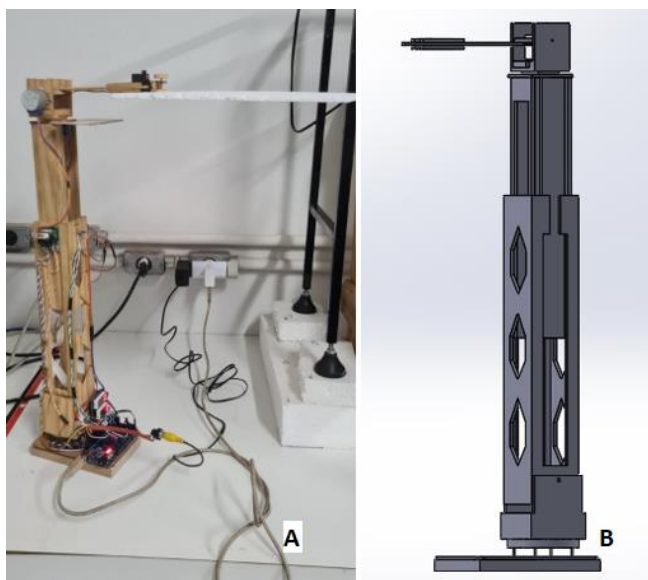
Desenho técnico protótipo em MDF no SolidWorks®.
